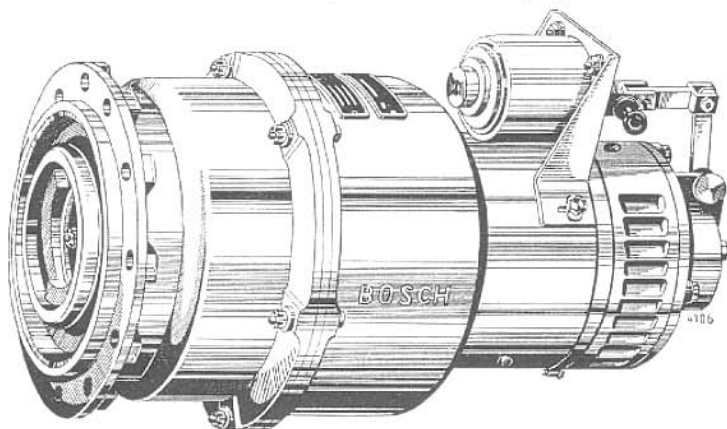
Bosch-Schwungkraft-Anlasser AL/SQB
